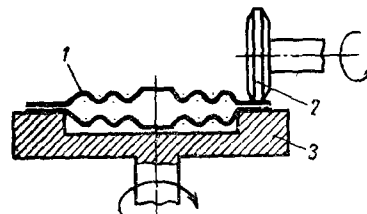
Контактная сварка мембранного чувствительного элемента:
